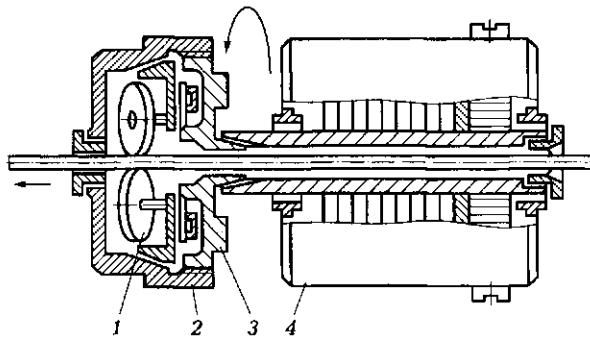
Схема безредукторного подающего механизма «Изаплан»:
